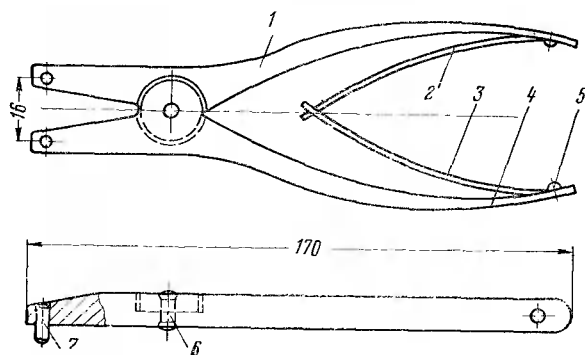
Клещи для установки стопорного кольца заднего подшипника ведущей шестерни:
